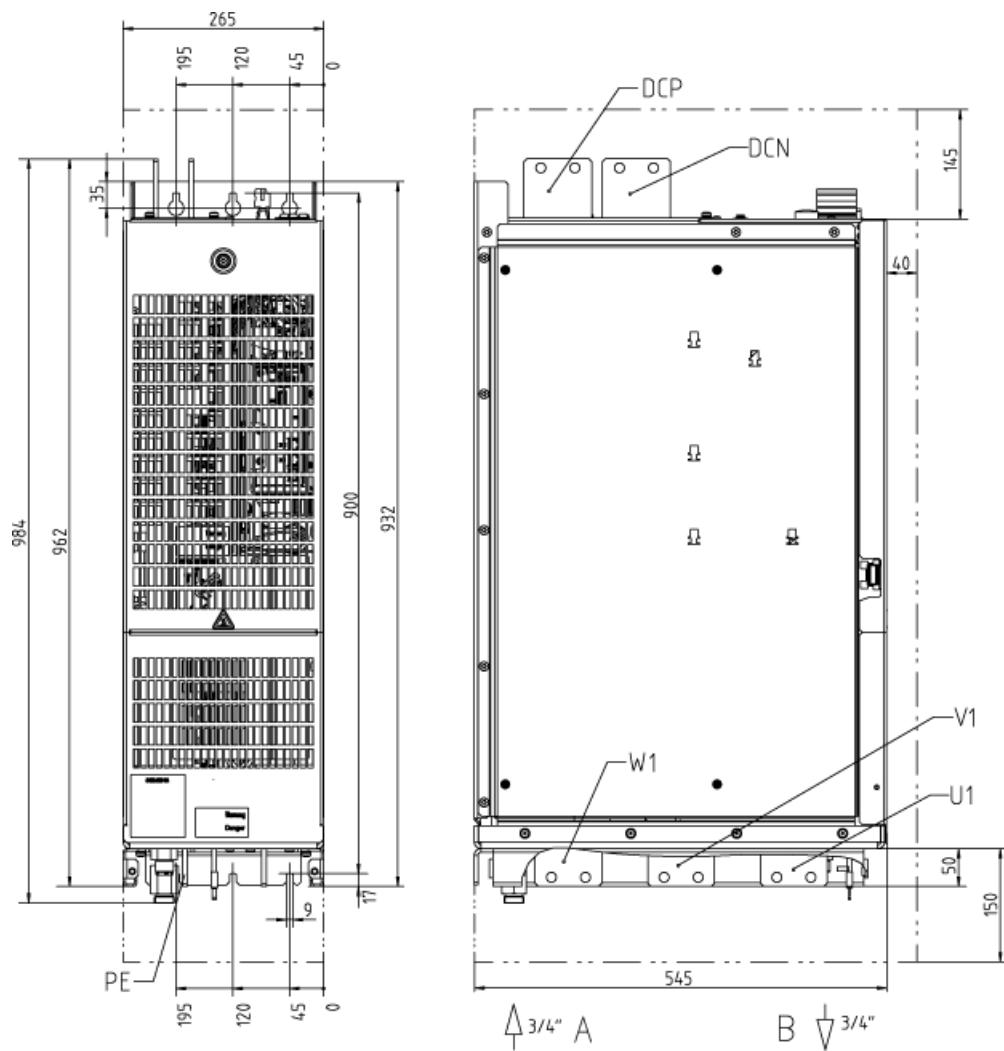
HXL 型调节型电源模块的外形尺寸图：正视图和侧视图
